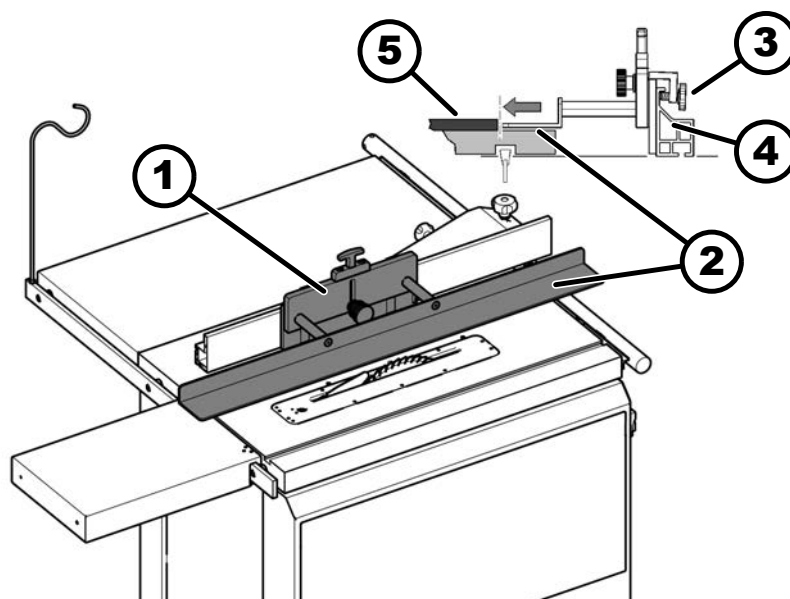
Montage de la butée auxiliaire "Sägeboy"
